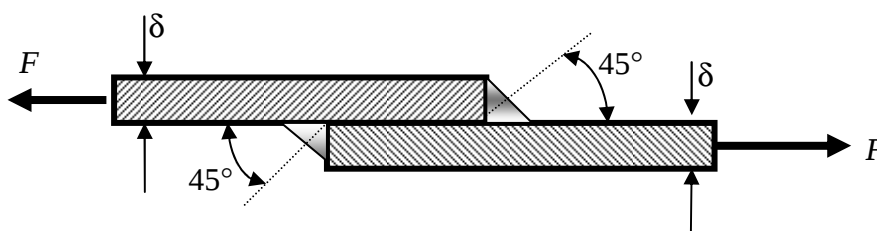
Схема нагружения углового лобового сварного шва
